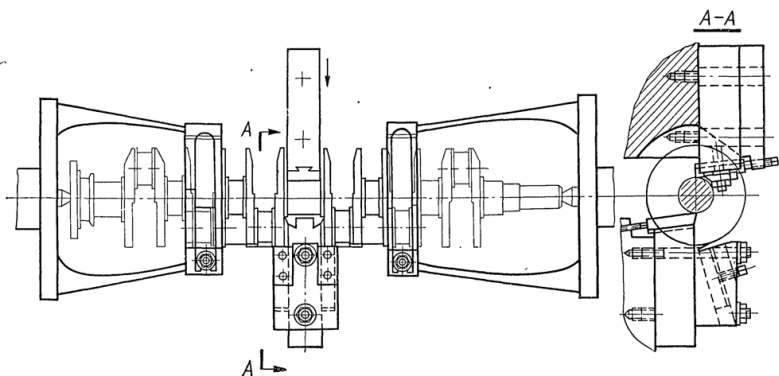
Обработка средней коренной шейки коленчатого вала на токарном многорезцовом станке
